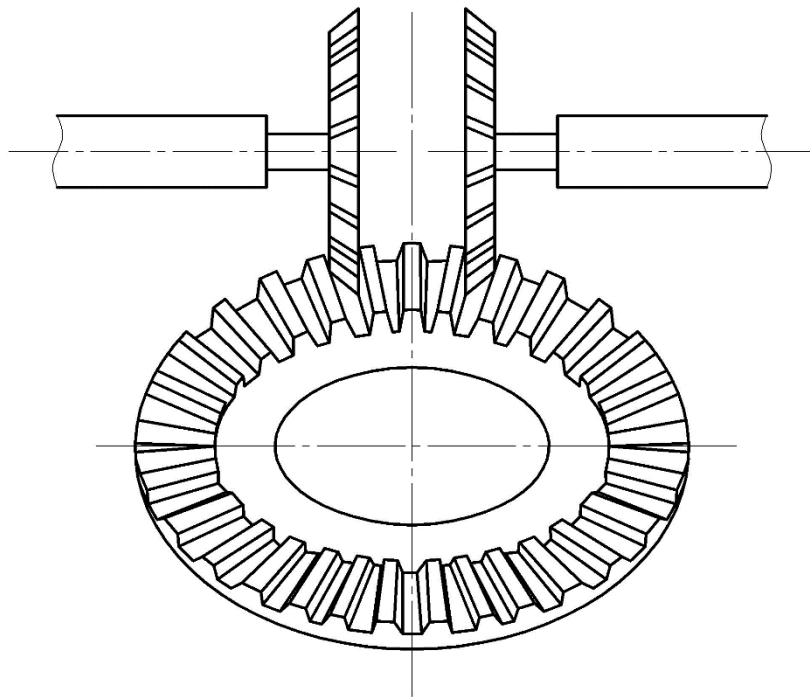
Схема попереднього фрезерування зубів двома дисковими фрезами
